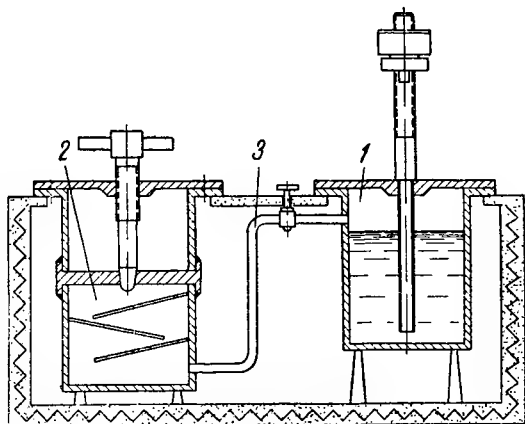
Схема приспособления для заливки литейного аппарата под вакуумом.
